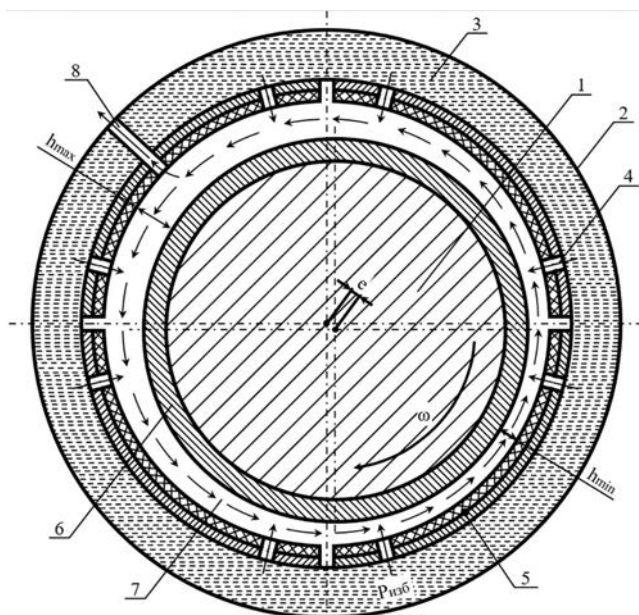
Схема перспективного подшипника скольжения: 1 – вал; 2 – корпус подшипника; 3 – масляный коллектор; 4 – каналы подачи смазочного масла во вкладышах; 5 – пористые керамические вкладыши, установленные на подложке из металла (4 сегмента); 6 – вставка с развитием поверхности контакта вала и смазочного масла; 7 – масляный зазор; 8 – канал отвода смазочного масла; e – эксцентриситет между центрами вала и подшипника; h_{\min} (h_{\max}) – минимальный (максимальный) зазор; $p_{\text{изг}}$ – избыточное давление подачи масла; ω – угловая частота вращения вала
